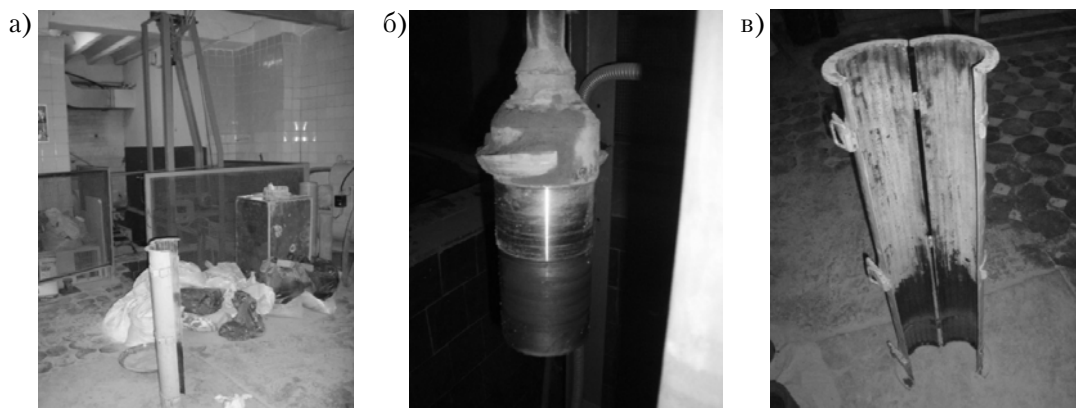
Экспериментальная установка для изготовления железобетонных труб: а – общий вид механизма формования; б – формующая головка; в – опалубочная форма.
